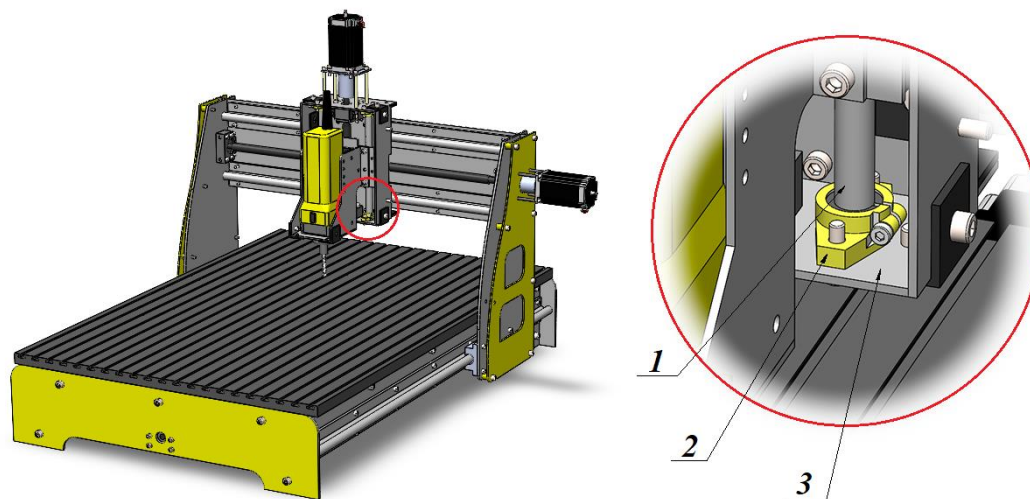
3D модель ЧПУ станка и рассматриваемого узла:
